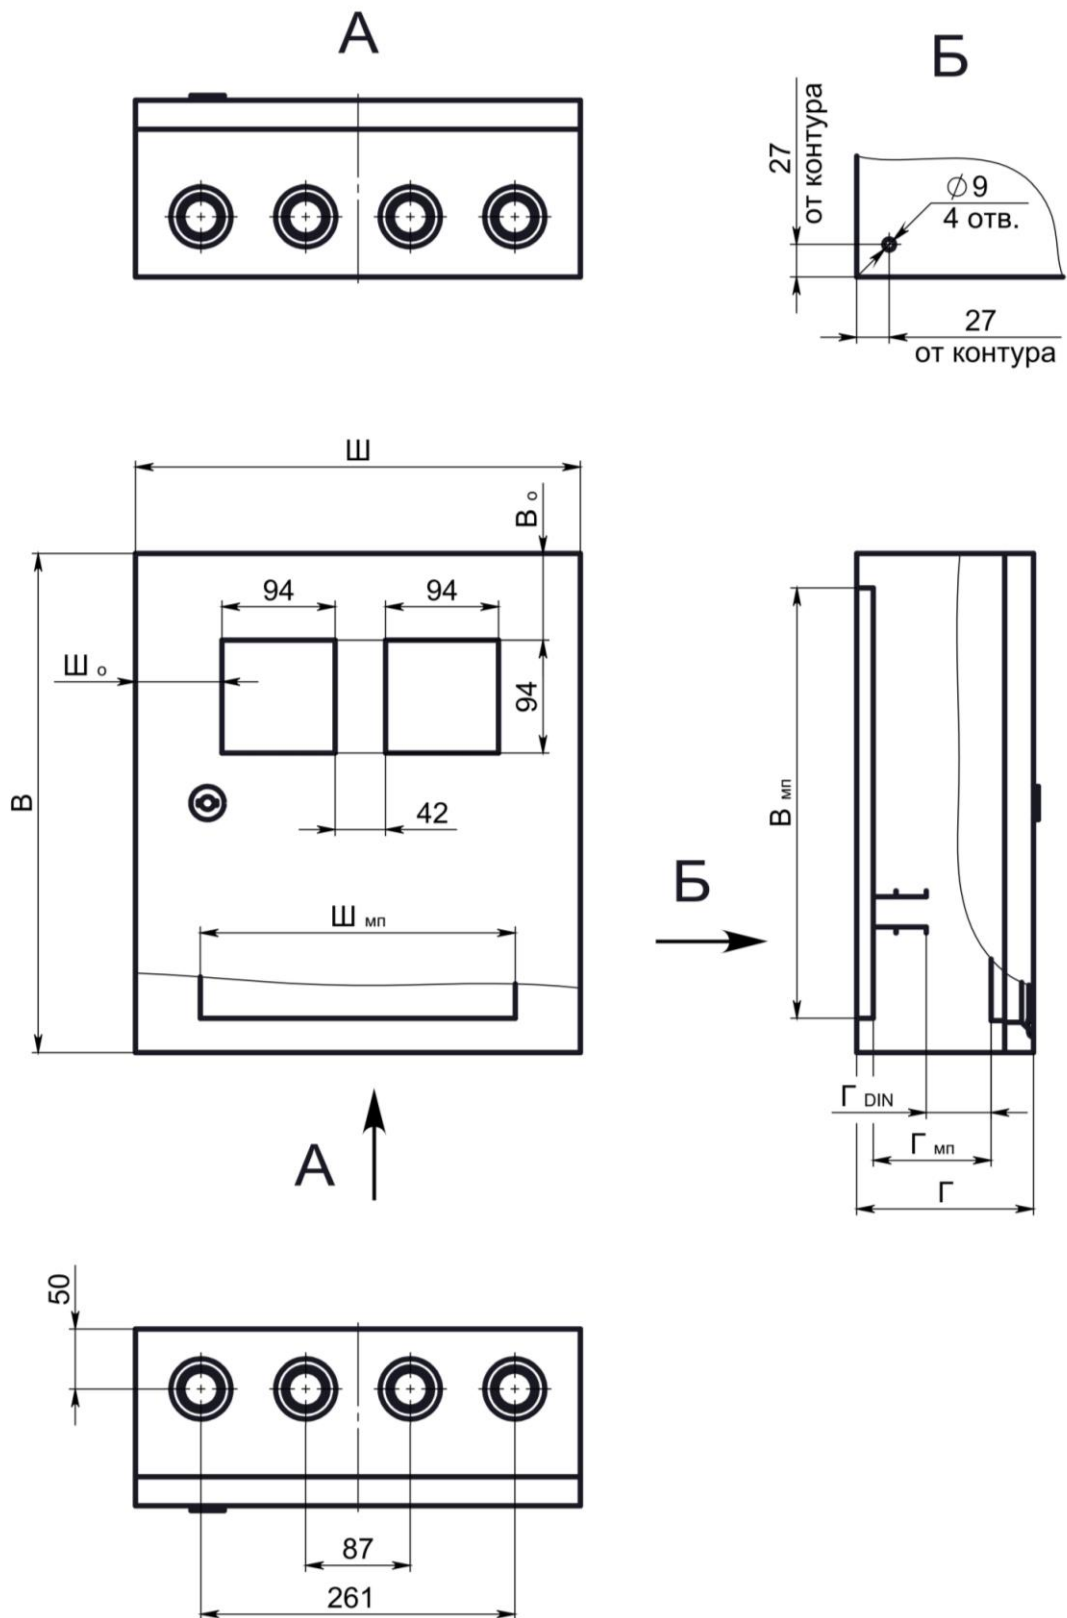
Габаритные, установочные и присоединительные размеры корпуса ЩУРН-ПРО-1х2-МП/7-415х370х147-IP66-УХЛ1 (код 367474)
